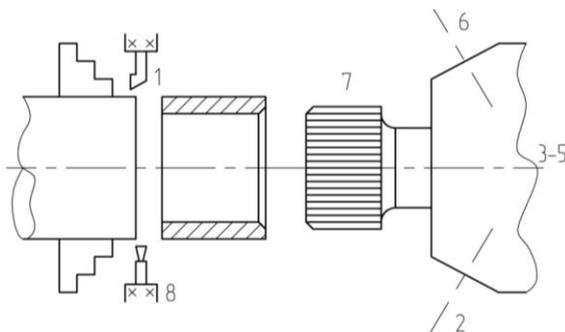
Пример обработки втулки за один установ на токарно-револьверном станке
